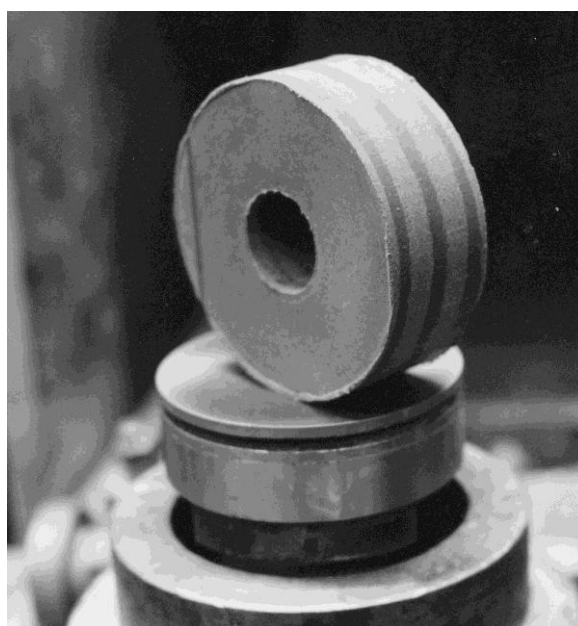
Заготовка, полученная по схеме двухстадийного прессования
